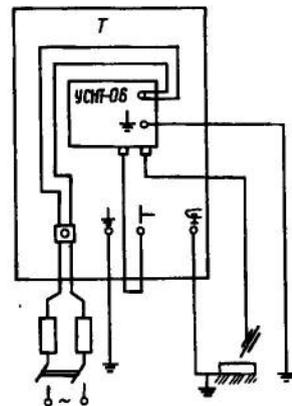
Схема підключення обмежувача неробочого ходу УСНТ-06 до зварювального трансформатора
